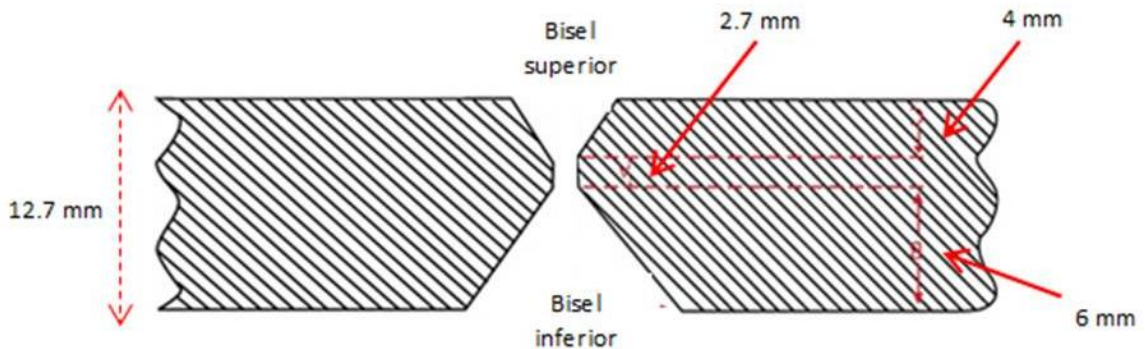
1 Dimensiones del biselado de las probetas soldadas.
